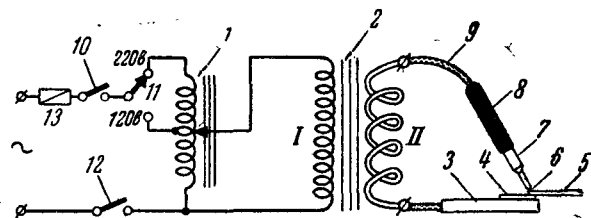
Простая схема устройства для точечной сварки.
